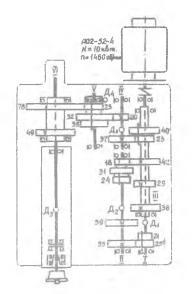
Кинематическая схема привода продольно-фрезерного станка мод. 6606
